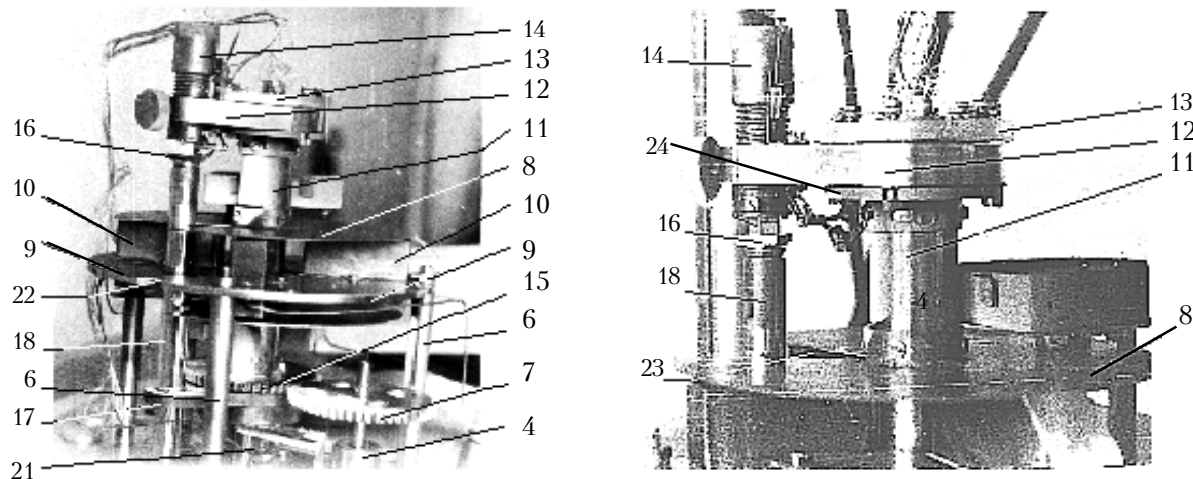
Устройство диффузионной термокомпрессионной сварки
